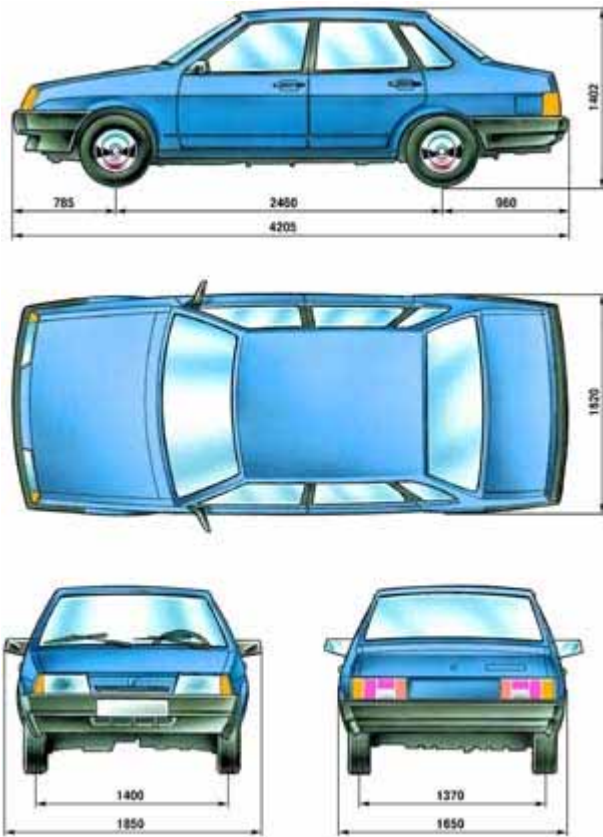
Габаритные размеры автомобиля ВАЗ–21099
